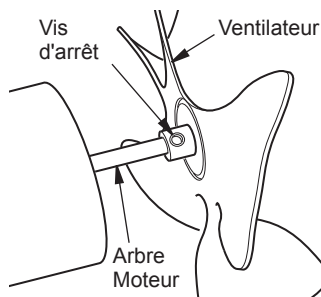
Emplacement du ventilateur, de l'arbre moteur et des vis d'arrêt
